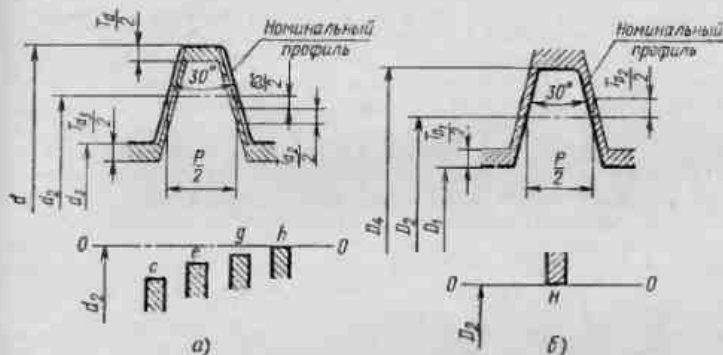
Расположение полей допусков однозаходной трапецидальной резьбы
